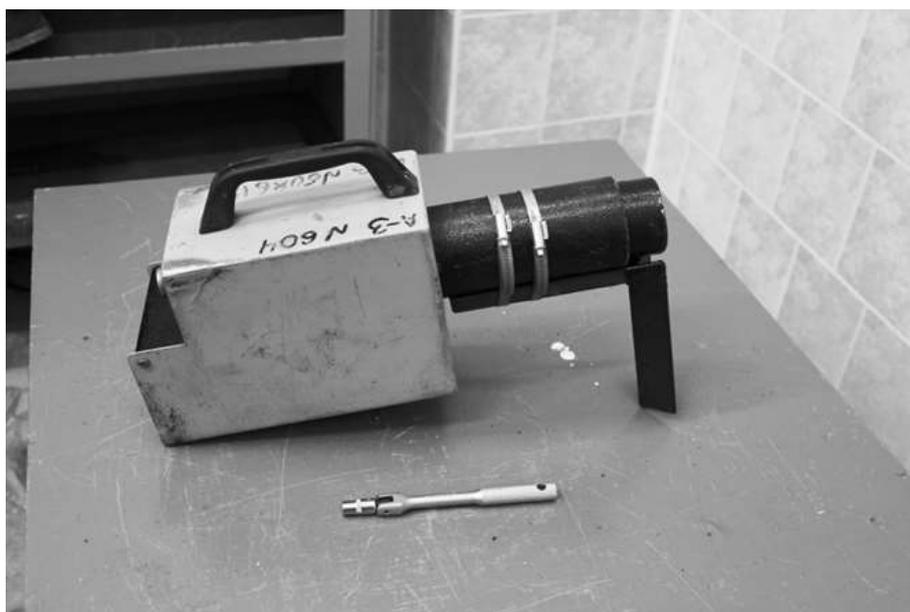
излучатель рентгеновских лучей устанавливается непосредственно на обращенную к источнику поверхность сварного соединения
